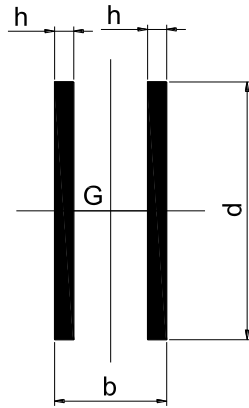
Cordón soldadura anclaje sup. de suspensión
